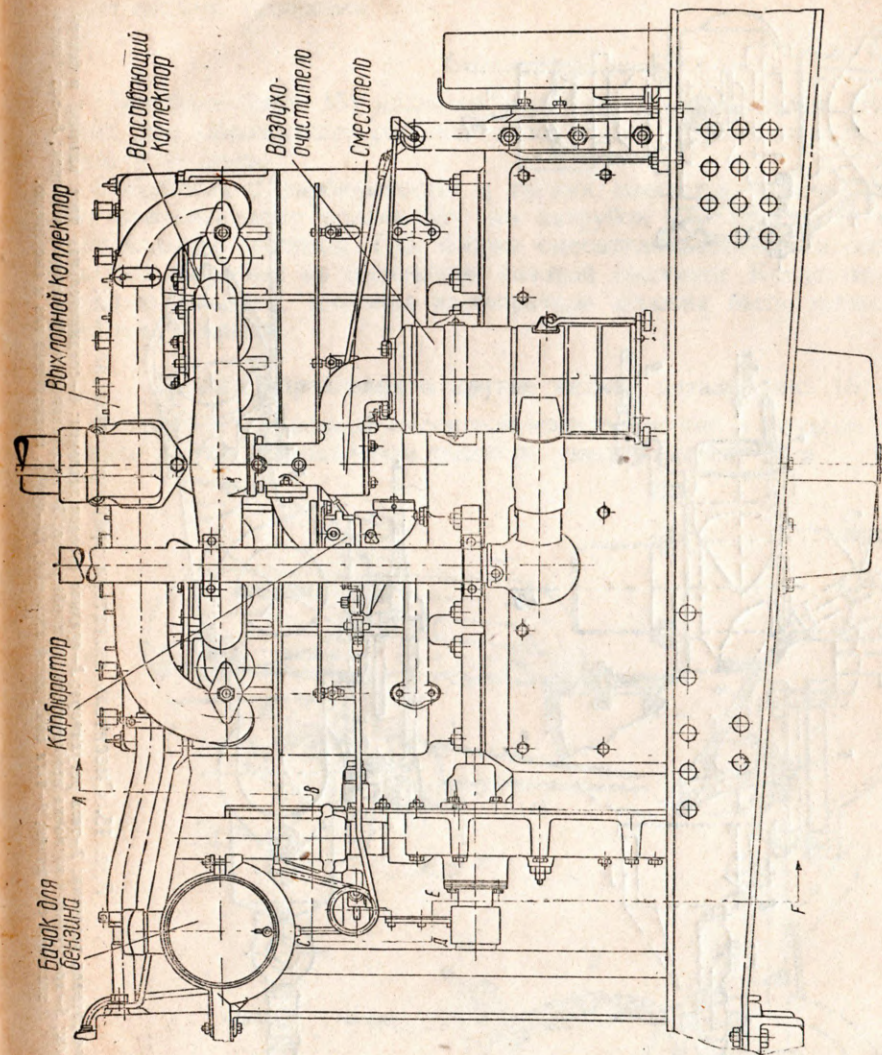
Двигатель трактора «сталинец-60», переоборудованного для работы на древесном газе
